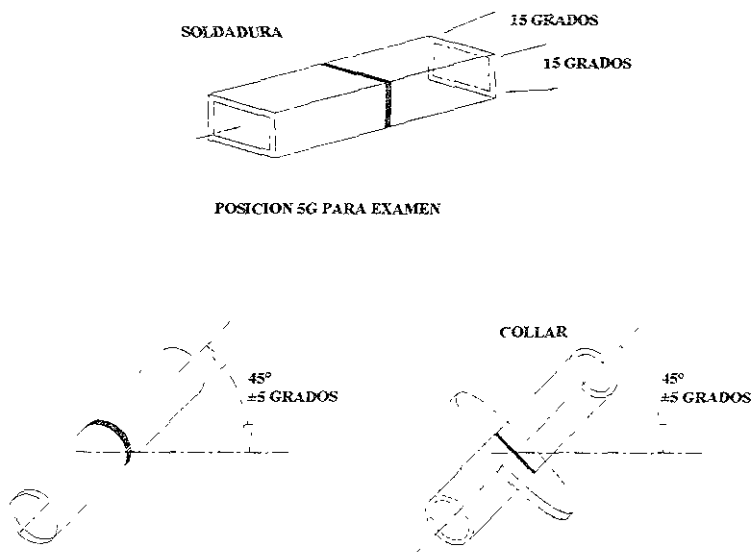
Piezas para prueba de un tubo soldado
